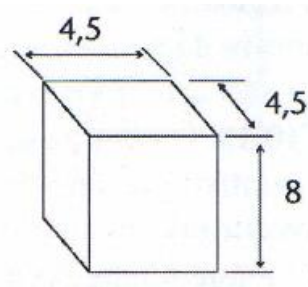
Geometria e dimensões (mm) de provete cúbico para ensaio de compressão segundo a norma NF T 51-10 [24]
